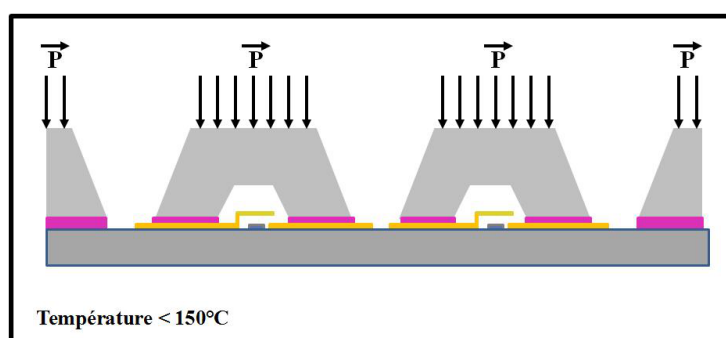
Soudure par thermocompression des deux wafers.
